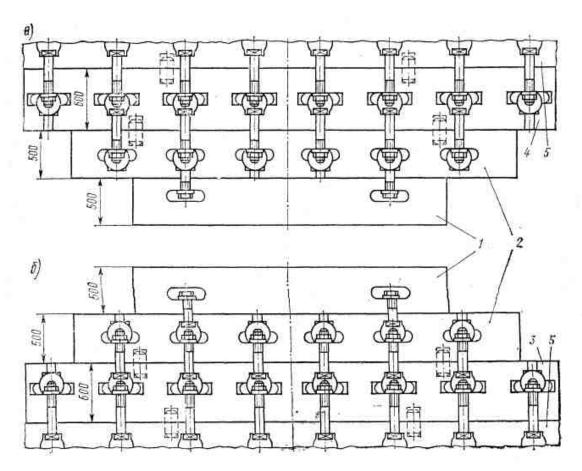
Схема штамповочного набора мощного гидравлического пресса: а – верхний набор; б – нижний набор; 1 – штамп; 2 – штамподержатель; 3, 4 – промежуточные плиты; 5 – опорные плиты стола и подвижной поперечины
